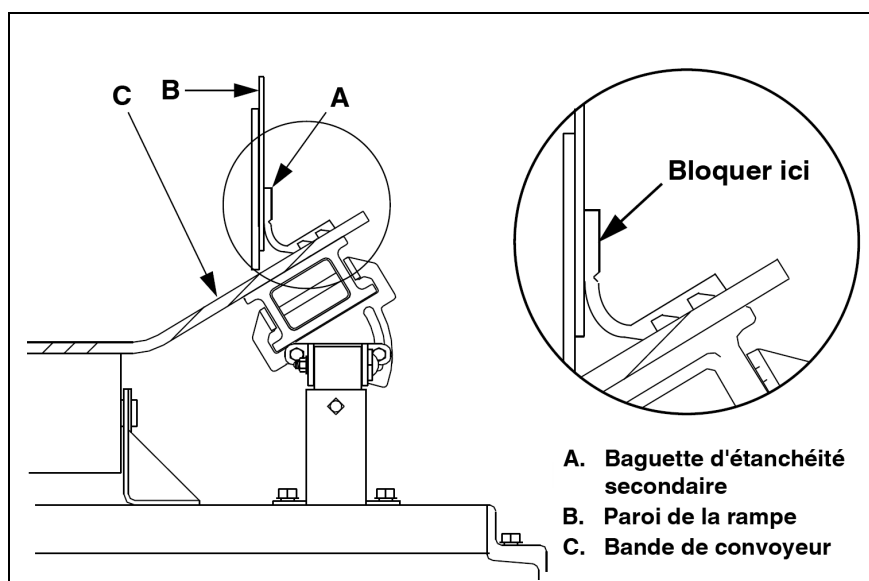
Installation de la baguette d'étanchéité secondaire en caoutchouc
